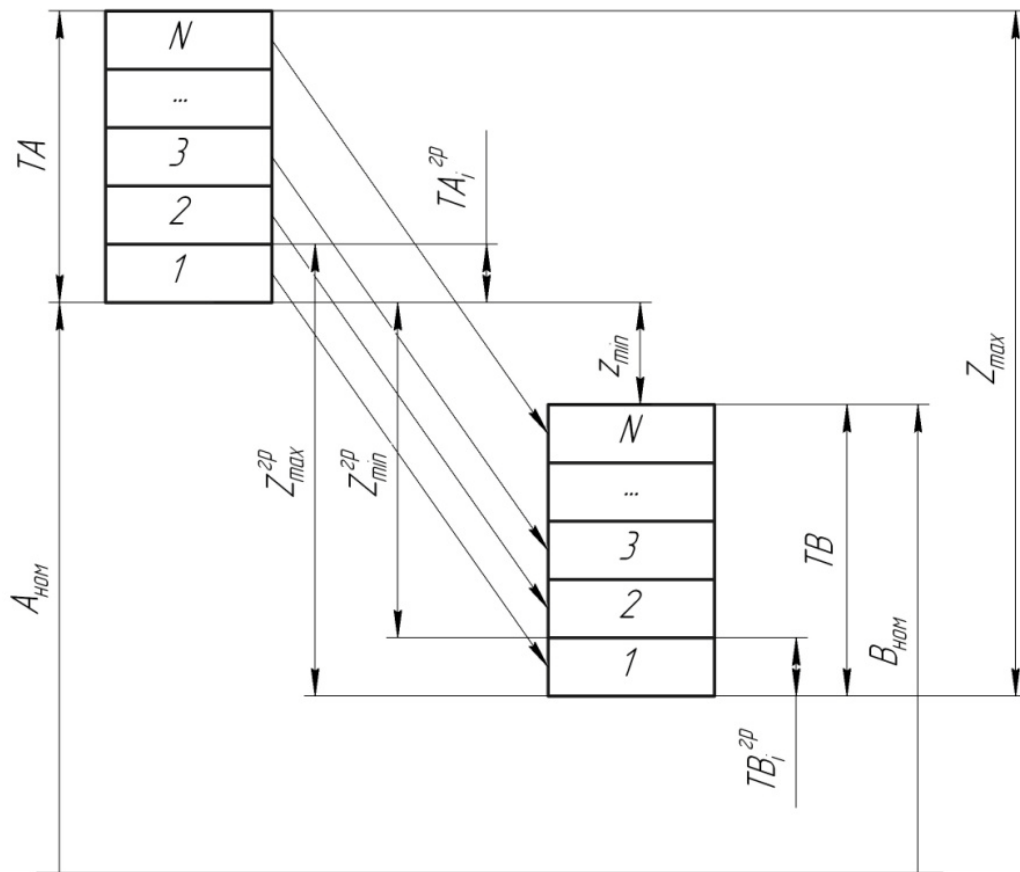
Схема соединения вал-втулка и разбивка допусков размеров вала и отверстия на группы
